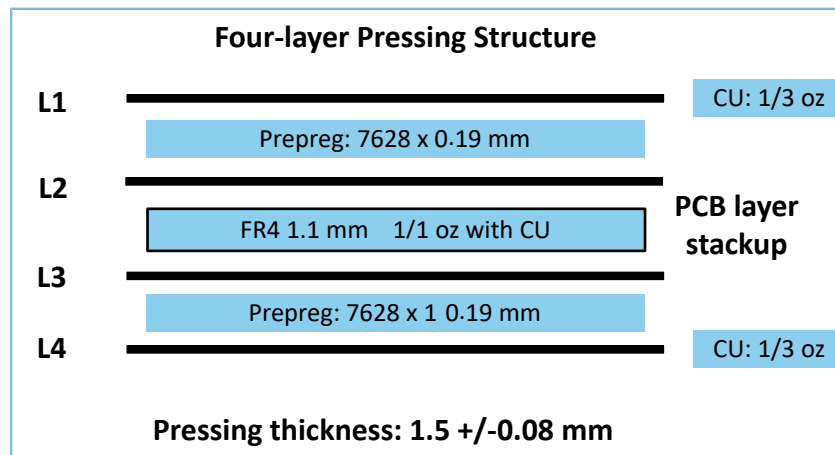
GR5526 PCB推荐叠层结构（QFN68）
